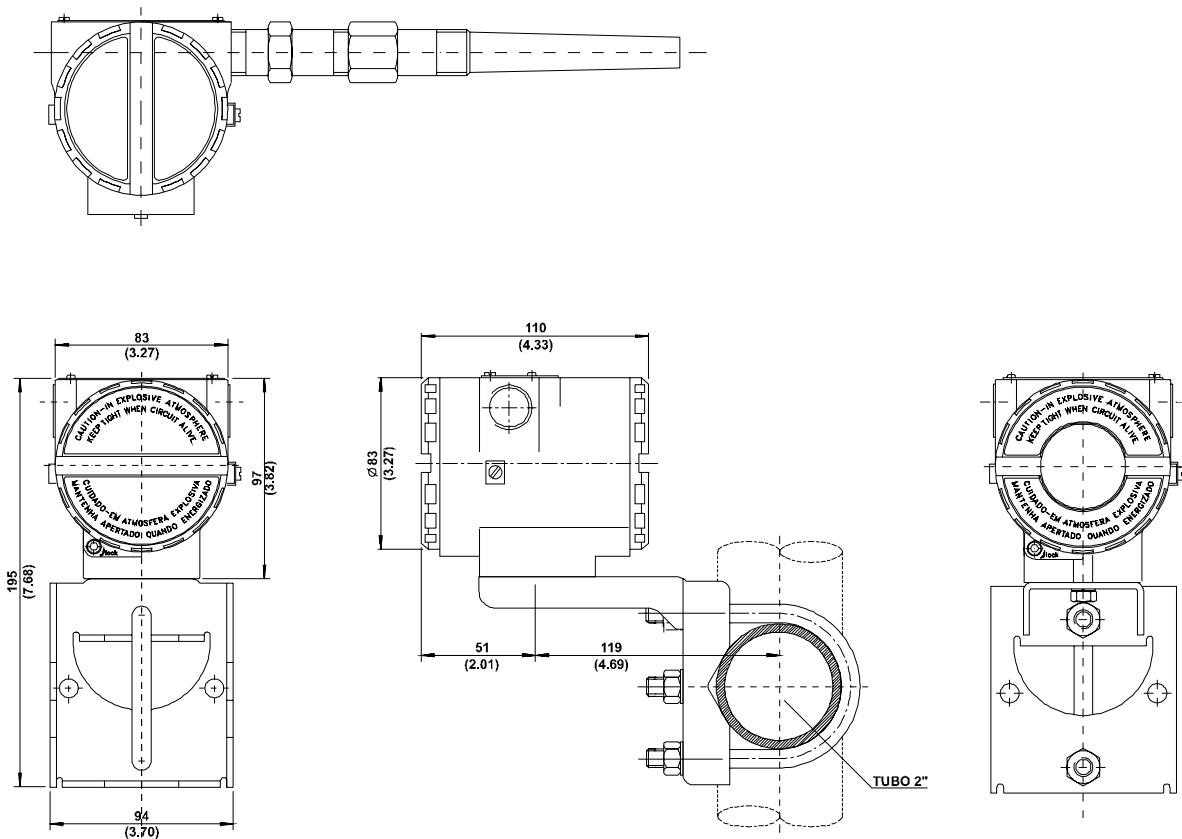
Desenho Dimensional e Posições de Montagem
